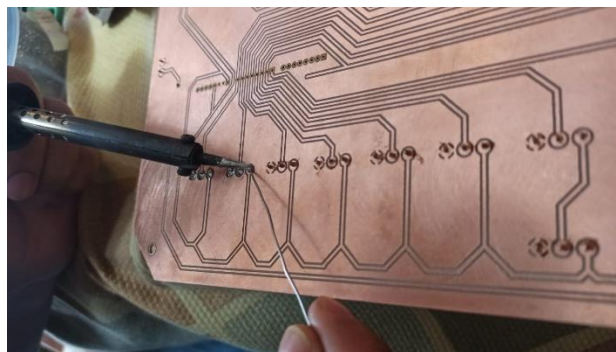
Proceso de soldadura en placa de sensores
